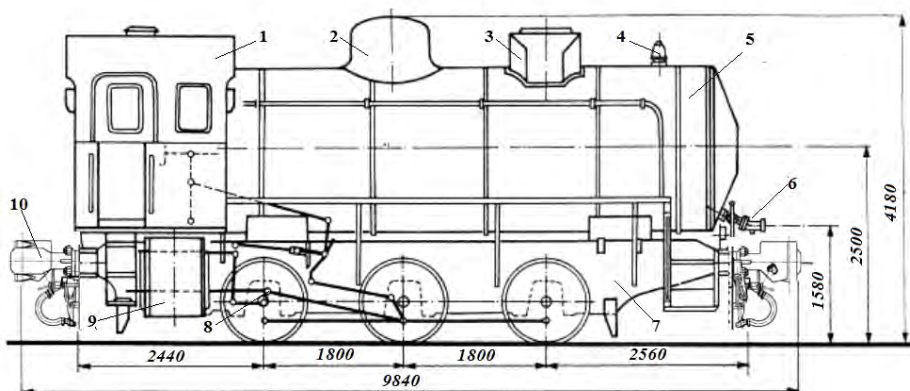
Схема и габаритные размеры локомотива ПАЛ-9П:
